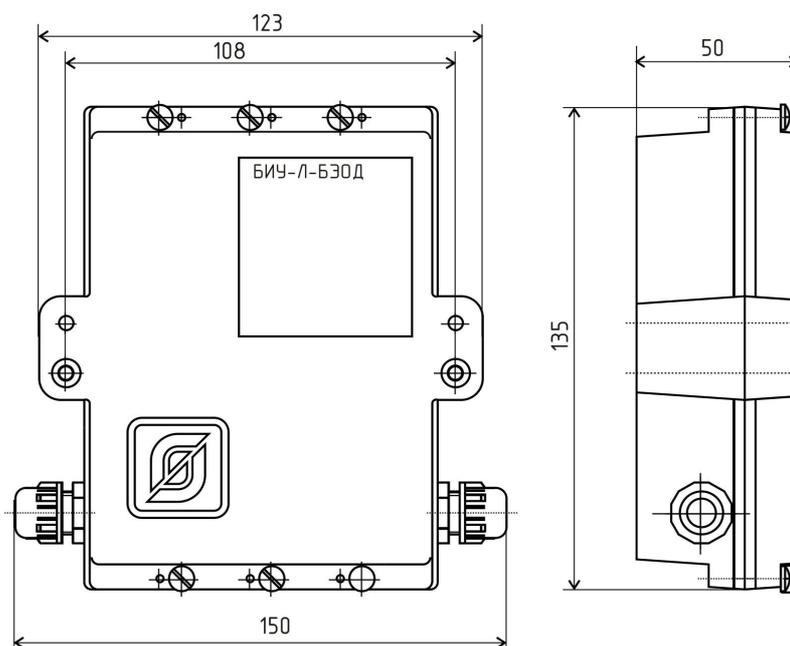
Габаритные размеры БИУ-Л-БЭОД
